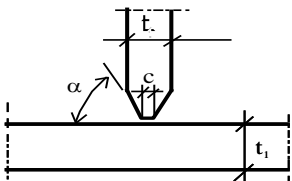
Chanfreins des soudures d'angle.
